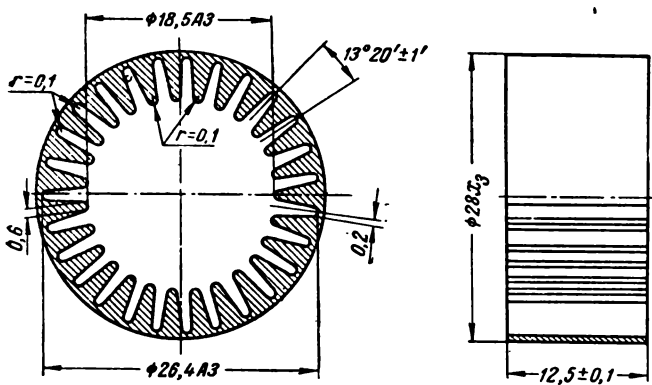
Металлокерамическая заготовка коллекторных пластин.
